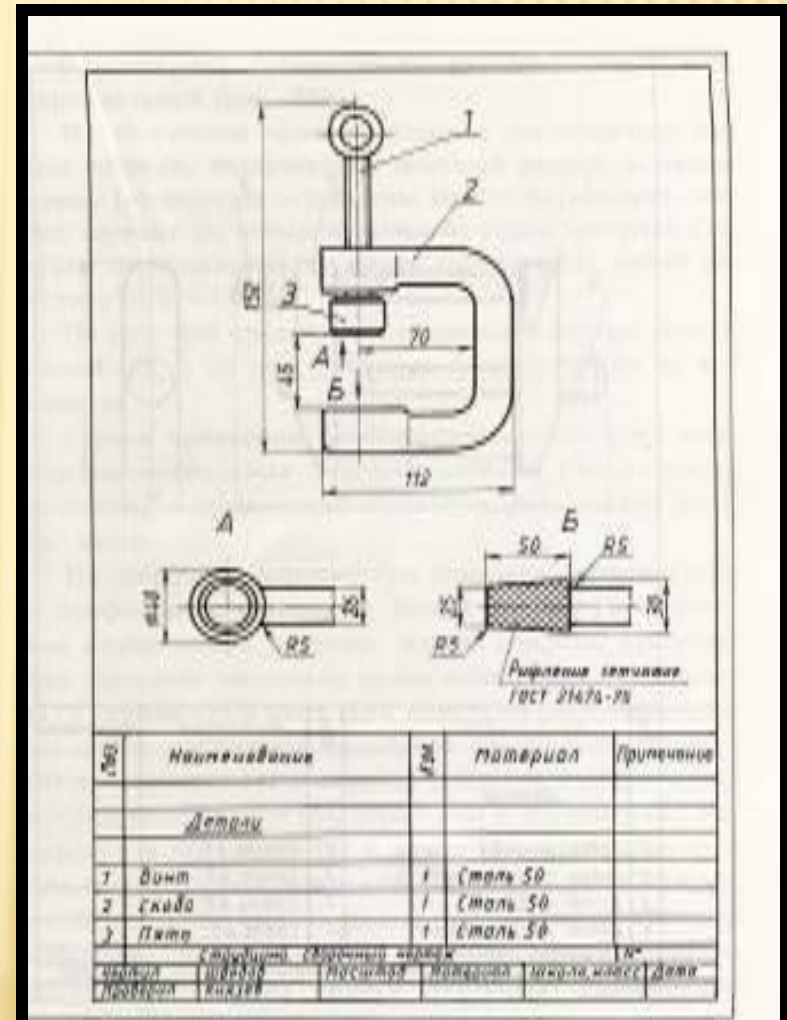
Струбцина свободнообразная. Сборочный чертеж
